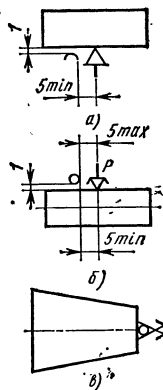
Обозначение рельефа рабочих поверхностей (рифленых, резьбовых, шлицевых и т. п.) опор, зажимов, установочных устройств
